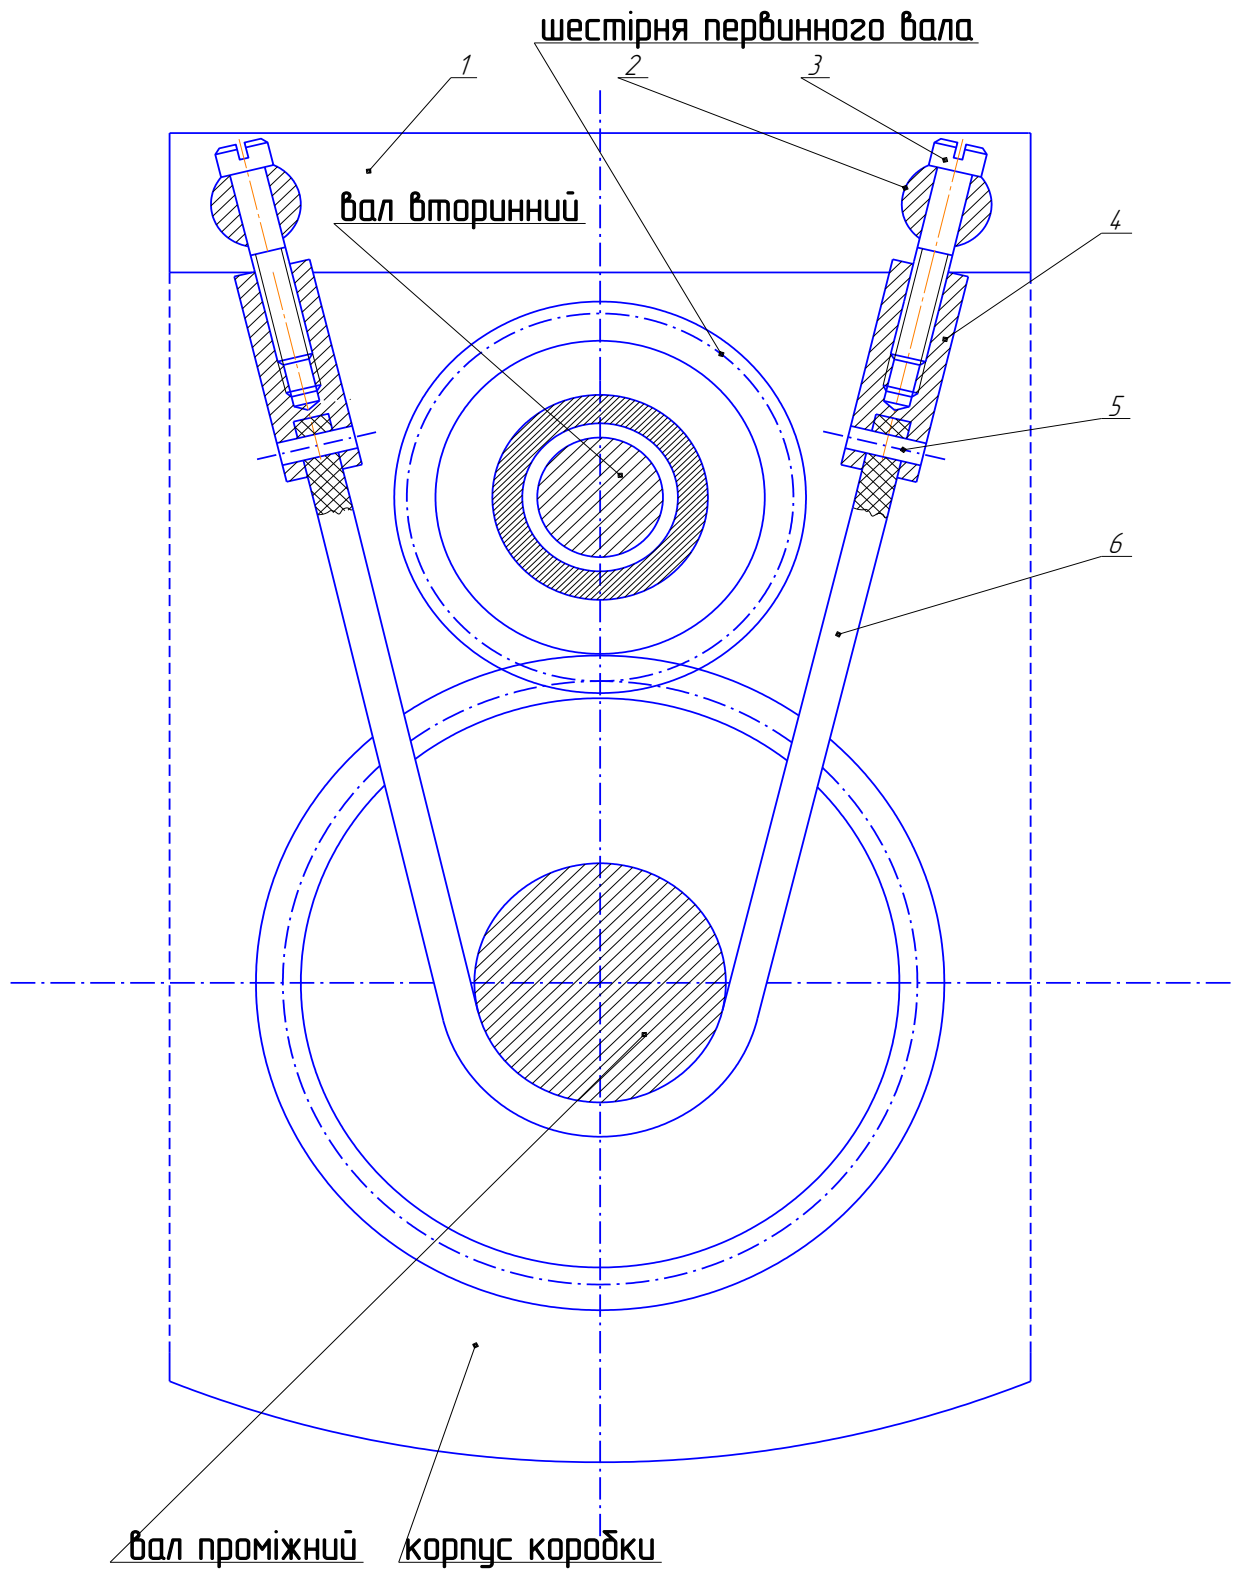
Фіксування шестерень проміжного вала у верхньому крайньому положенні
